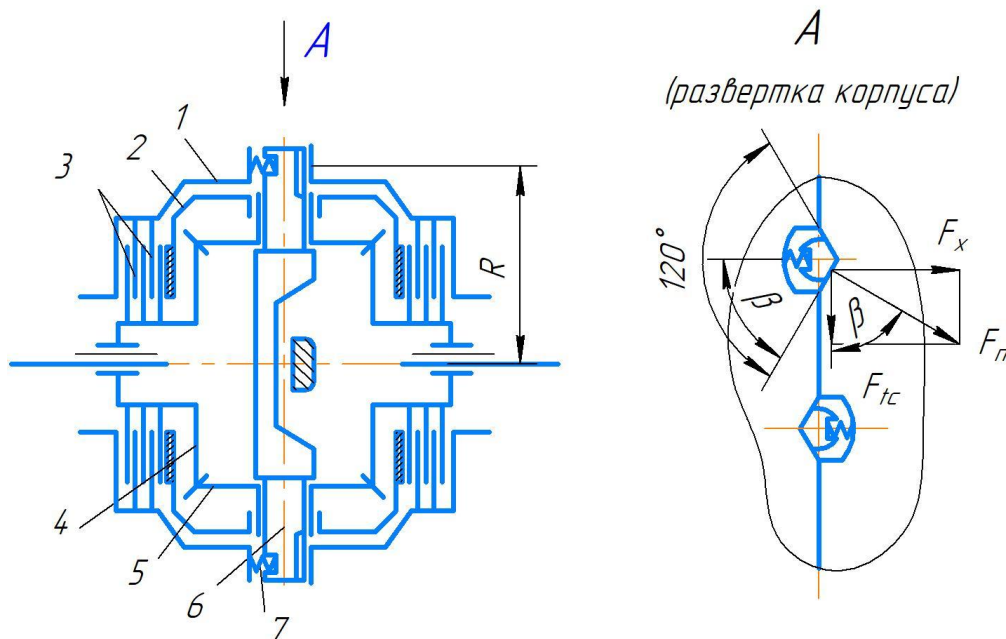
Схема модернизированного самоблокирующегося дифференциала повышенного трения «Power Lock»: 1 – корпус; 2 – чаша нажимная; 3 – комплект дисков; 4 – полуосевая шестерня; 5 – сателлит; 6 – ось сателлита; 7 – упругий элемент;  $R$  – радиус расположения равнодействующей окружной силы;  $\beta$  – половина угла скоса на корпусе дифференциала,  $\beta=60^\circ$ ;  $F_x$  – сила, сжимающая фрикционные диски;  $F_{tc}$  – окружная сила на скосах оси вращения сателлитов
